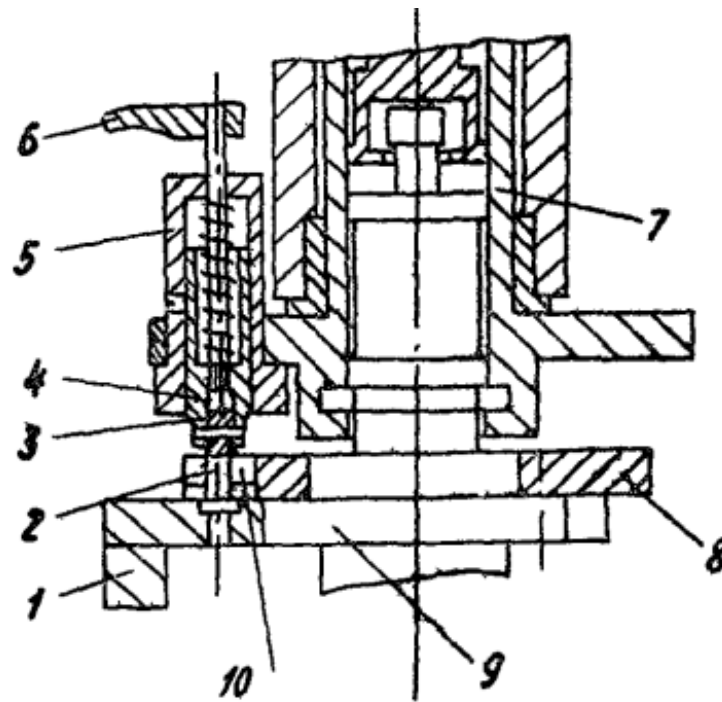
Механізм автоматичної заміни інструменту
